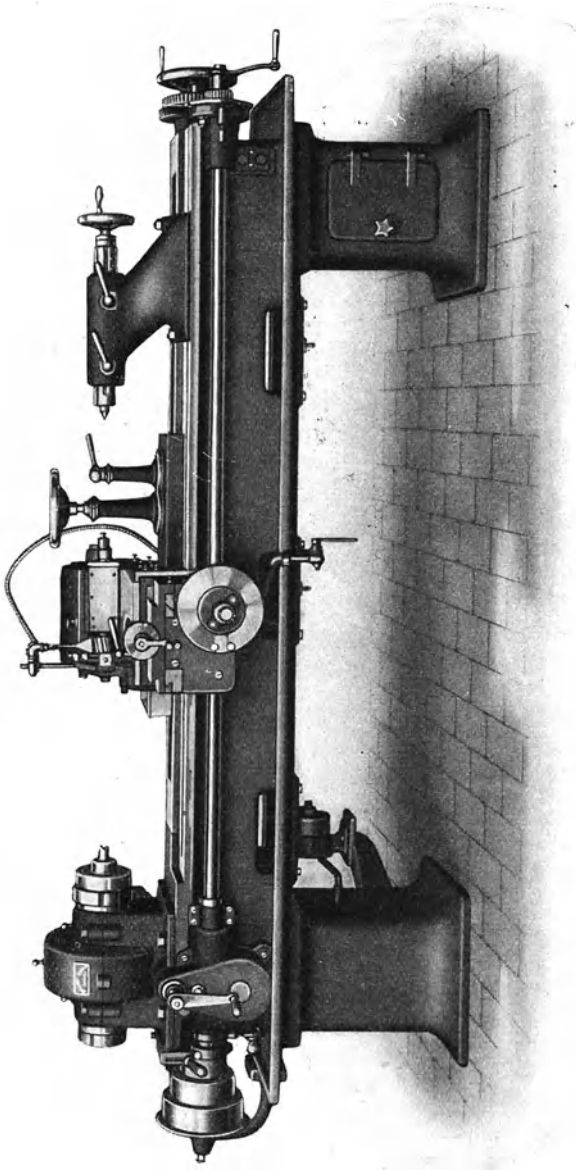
Die Gewindefräsmaschine von Schilling und Krämer.
